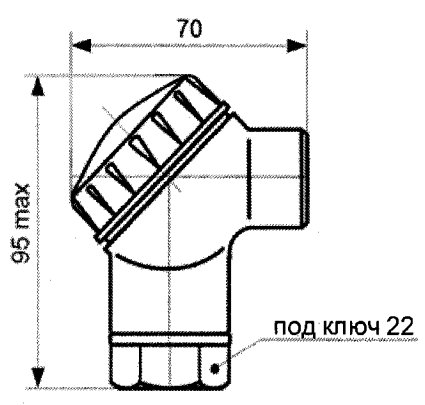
Кресленик зовнішньої частини ТСП-1390 з головкою типу ПБВИ.408724.003 СБ
